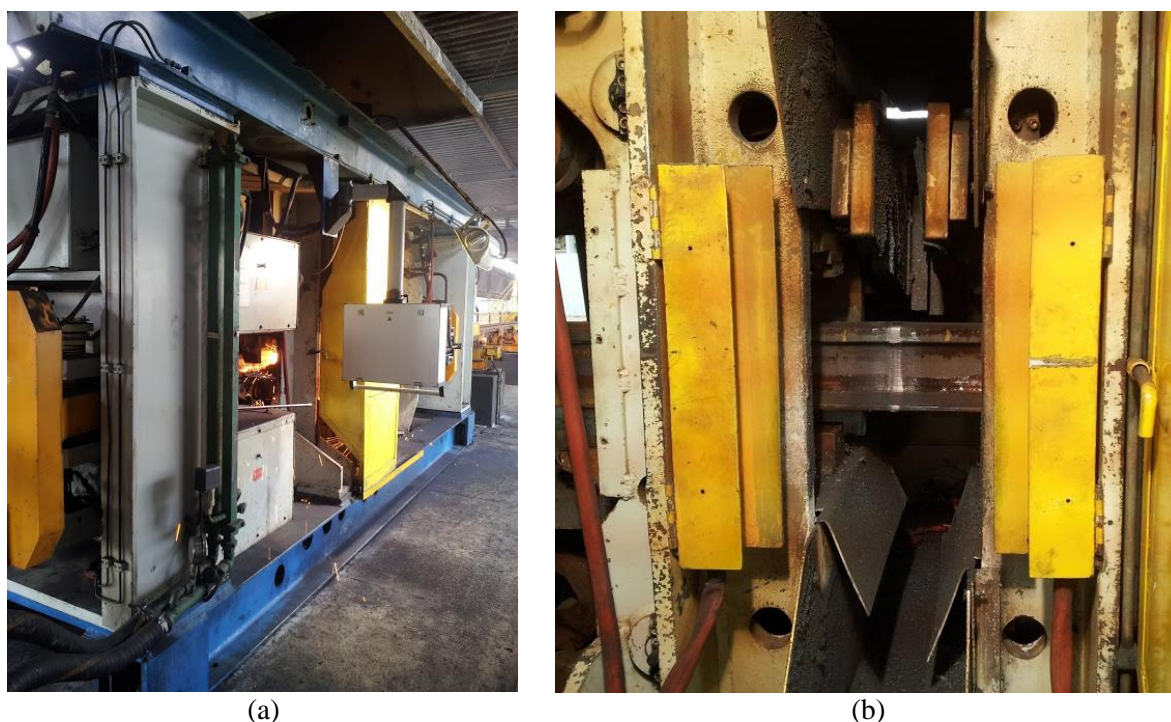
Máquina de soldagem elétrica por centelhamento marca Schlatter de propriedade da Empresa VLI. (a) Flash durante a soldagem; (b) Junta soldada após o corte automático de rebarbas.
